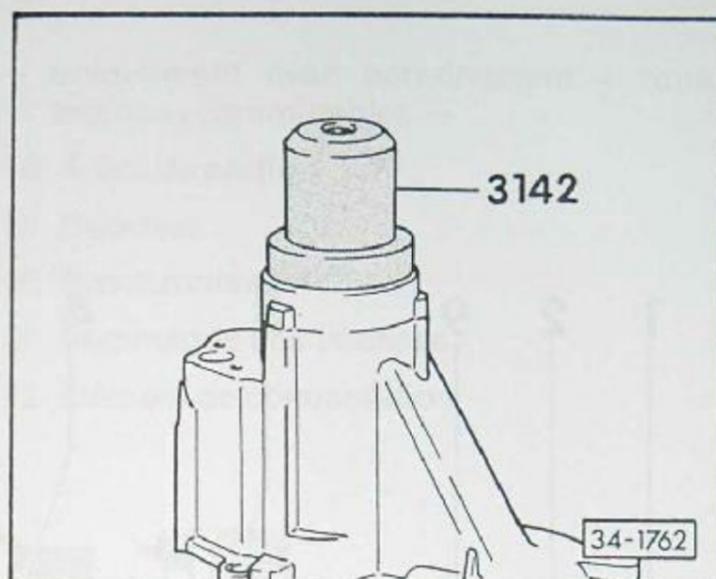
Bague-joint radiale: emmanchement à la presse jusqu'en butée
